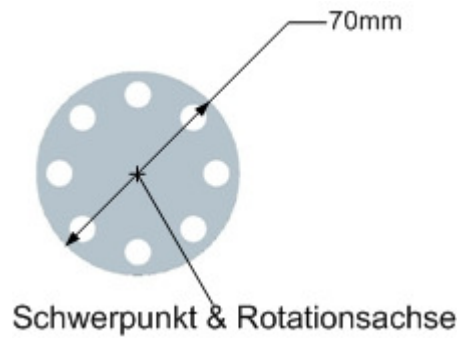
Erforderliche Größen zur Berechnung der Massenträgheit des Flansches, erstellt mit Pro Engineer Wildfire 4.0. Zu sehen sind: Rotationsachse und Schwerpunkt des Flansches sowie der Durchmesser des Flansches.
